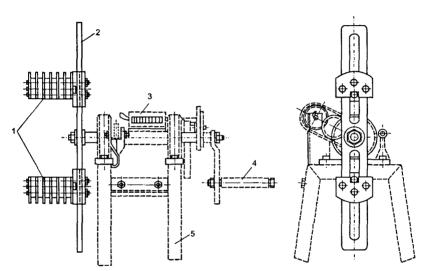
Станок для ручной намотки катушек с раздвижным шаблоном: 1 — колодка шаблона; 2 — диск; 3 — счетчик оборотов; 4 — рукоятка; 5 — станина
